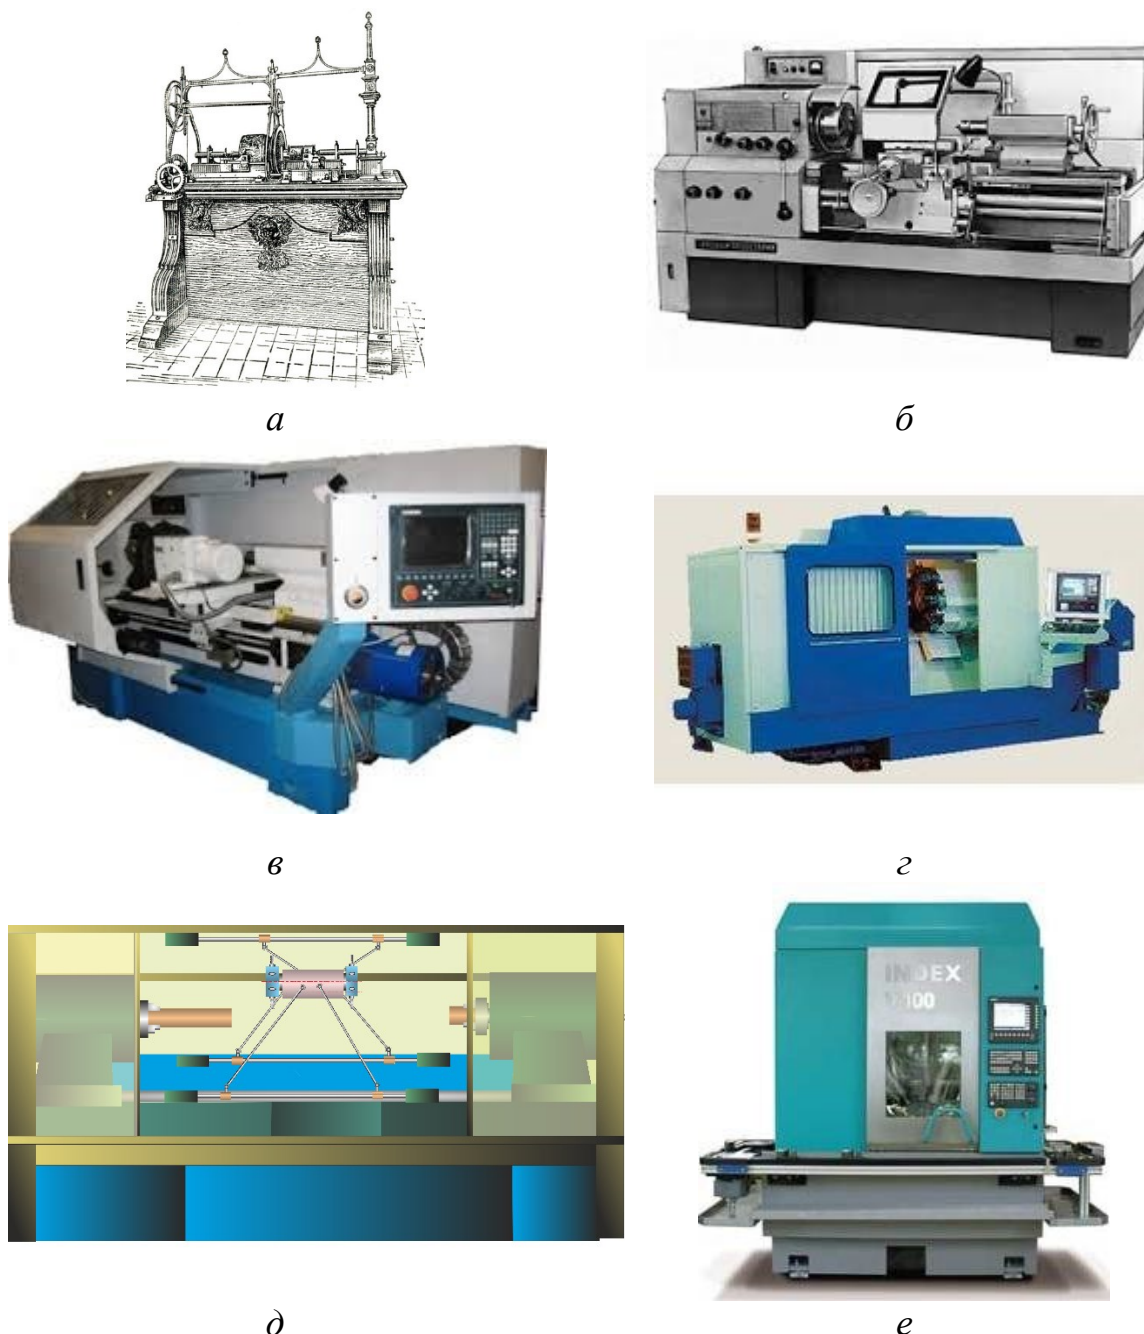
Примеры развития ТС металлорежущего токарного станка: *а* – первый в мире токарно-копировальный станок Андрея Нартова (1712 г.); *б* – токарно-винторезный станок 16К20 (1973 г.); *в* – токарный станок с ЧПУ 16К20Ф30 (1980 г.); *г* – многооперационный токарный центр 1П420ПФ40 с ЧПУ NC-201 (1990 г.); *д* – токарный многоцелевой станок на базе МПС с шестью штангами постоянной длины (2006 г.); *е* – станок VerticalLine V100 (Германия) на основе дельта-робота для трехкоординатной обработки (токарной, фрезерной, лазерной закалки, лазерной сварки, шлифования, операции сборки) (2015 г.)
